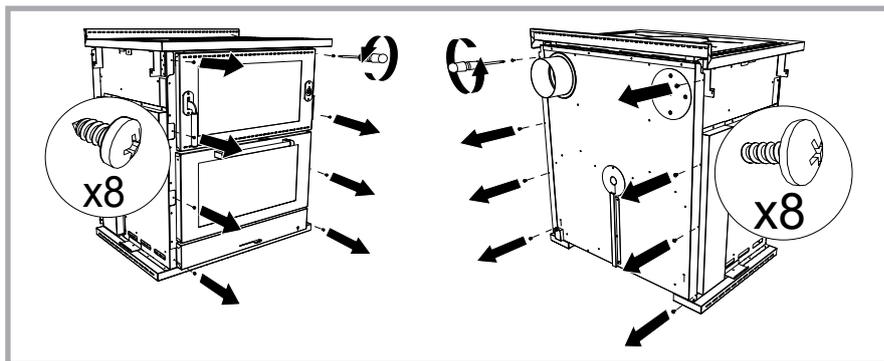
Position der Schrauben am Herd um die Seitenwände korrekt anzubringen.
